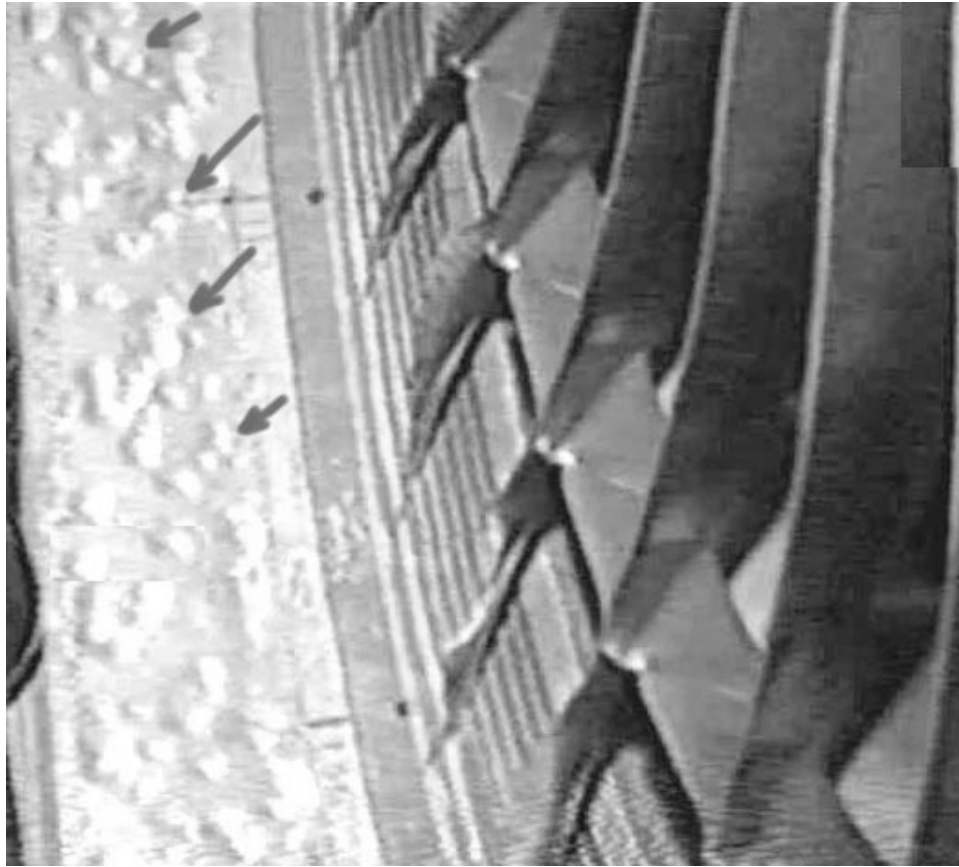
Bosselage du revêtement acoustique causé par le givre qui s'est détaché du rotor de la soufflante.
